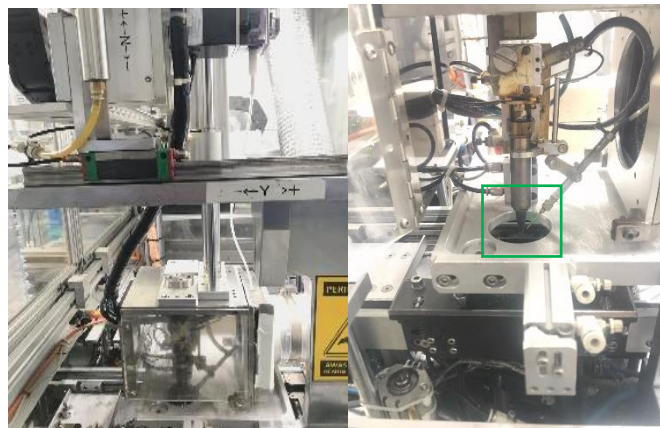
Tampak Depan & Samping *Tips Solder P3DR
